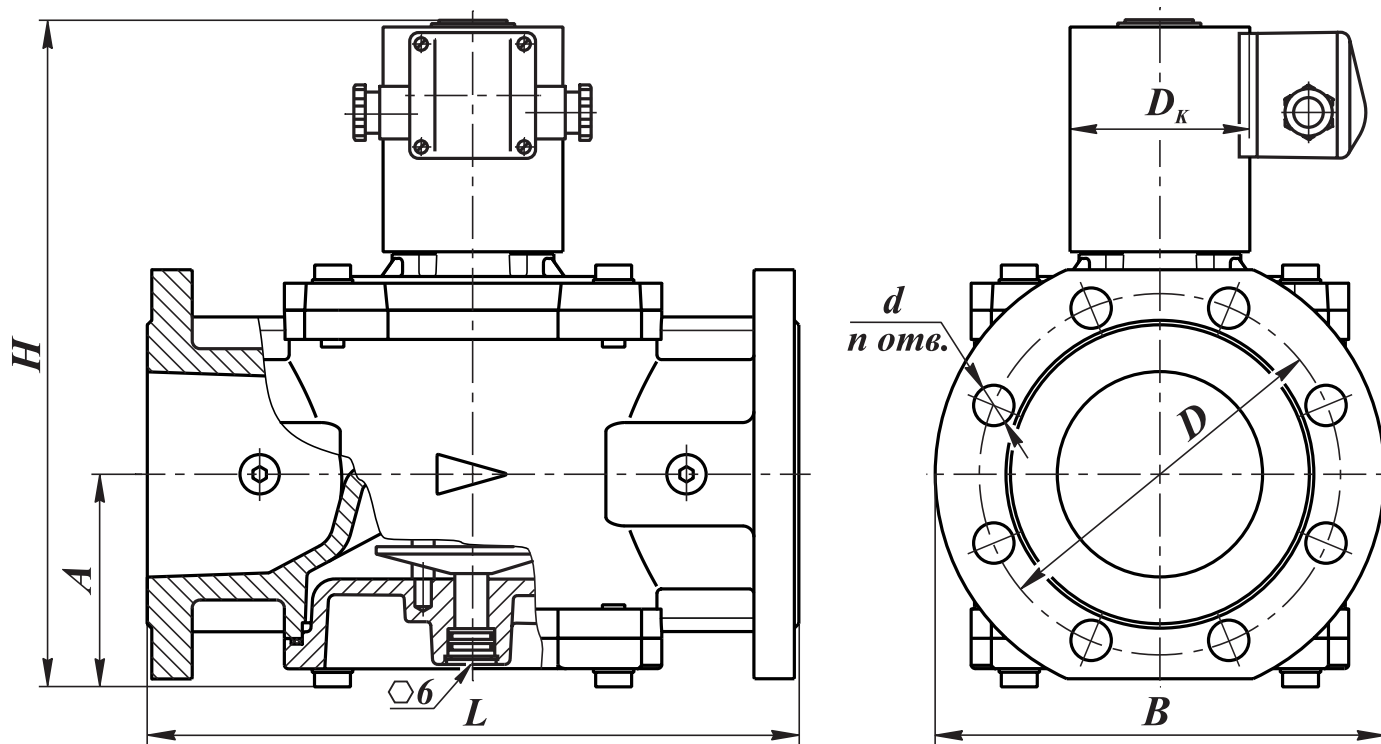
Клапаны на DN 65 - 100 фланцевые с ручным регулятором расхода (исполнение: с соединительными фланцами PN 16)
